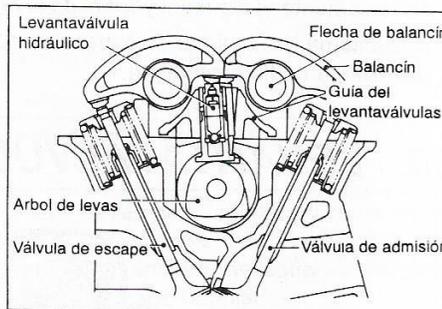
Posición para instalar el levantaválvulas hidráulico.
